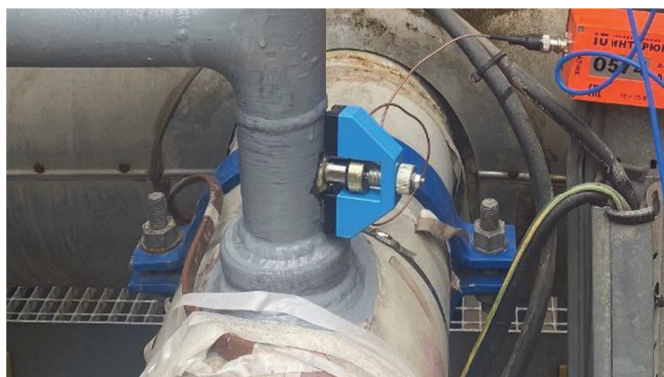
Внешний вид сварного шва трубопровода блока КЦА, в котором создавались недопустимые напряжения
